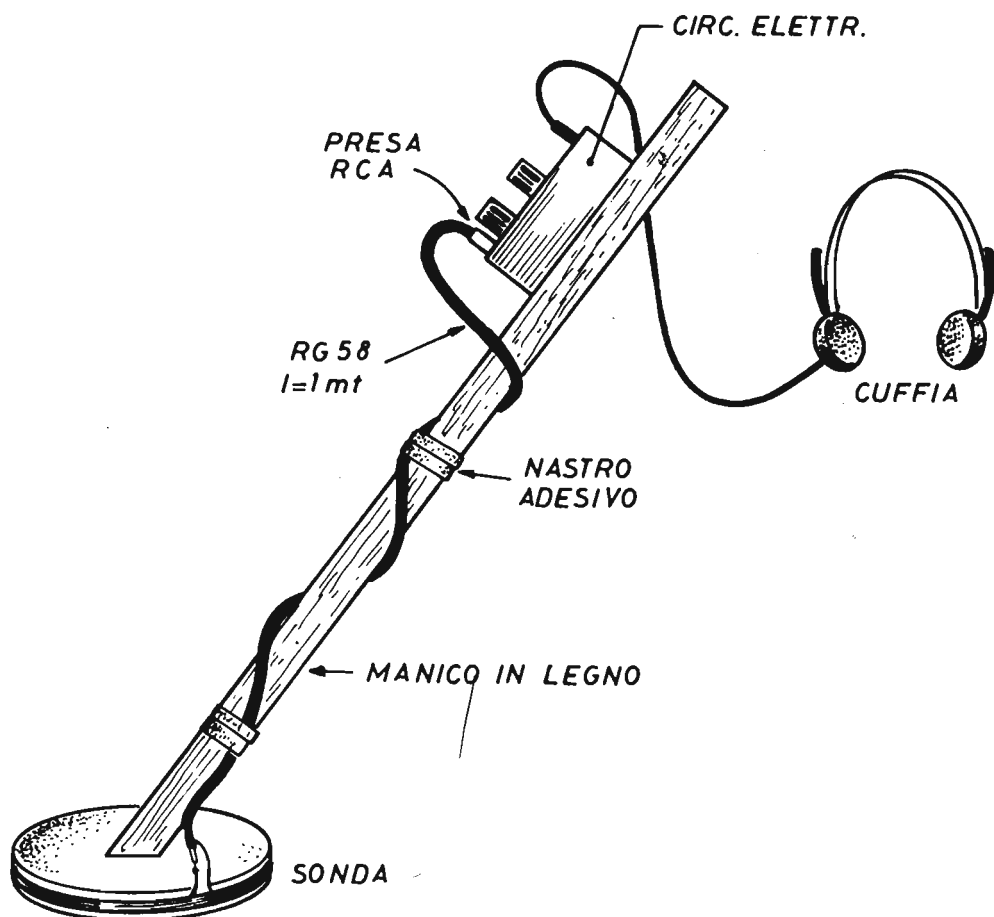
Montaggio completo del cercametalli realizzato su supporto di legno. La lunghezza del cavo RG58 deve essere, come indicato nel disegno, di un solo metro.
